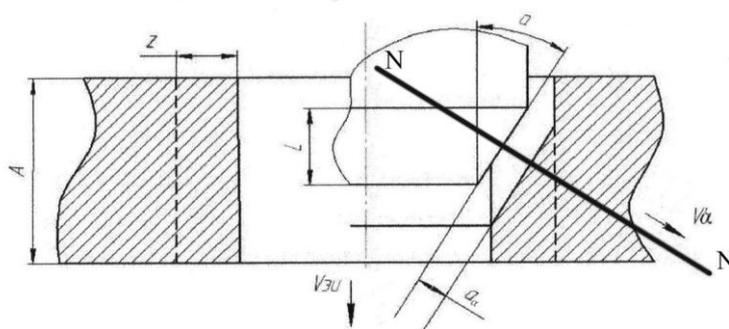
Обрабатываемое отверстие и рабочая часть ЭИ при калибровании
